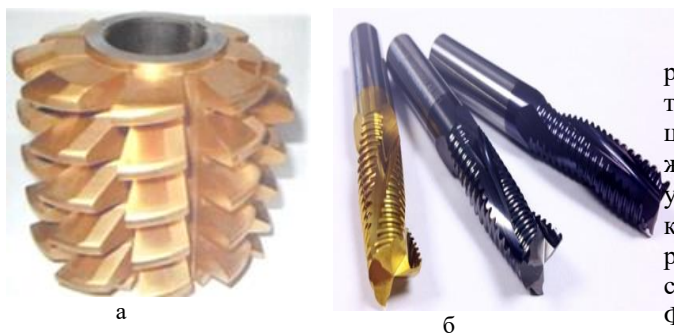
Металлорежущие инструменты с различными покрытиями
